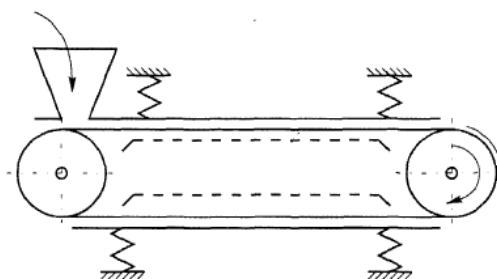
Кінематична схема обезкрилювача стрічкового типу
